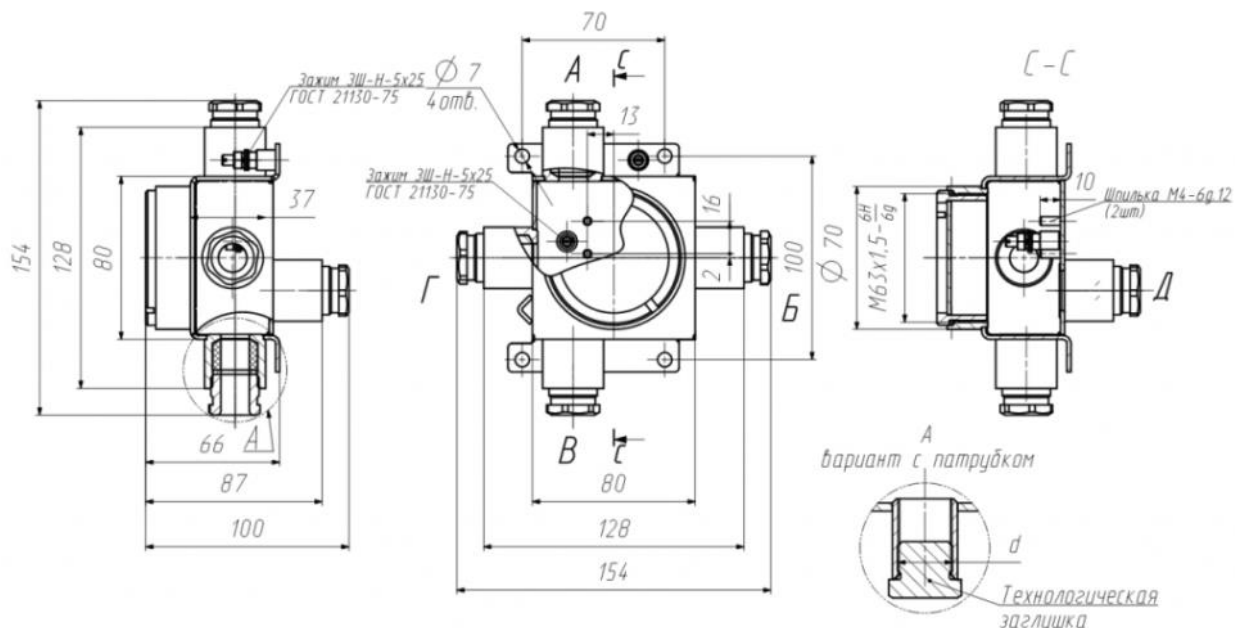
Общий вид коробок ЕхКК-Нм63/
